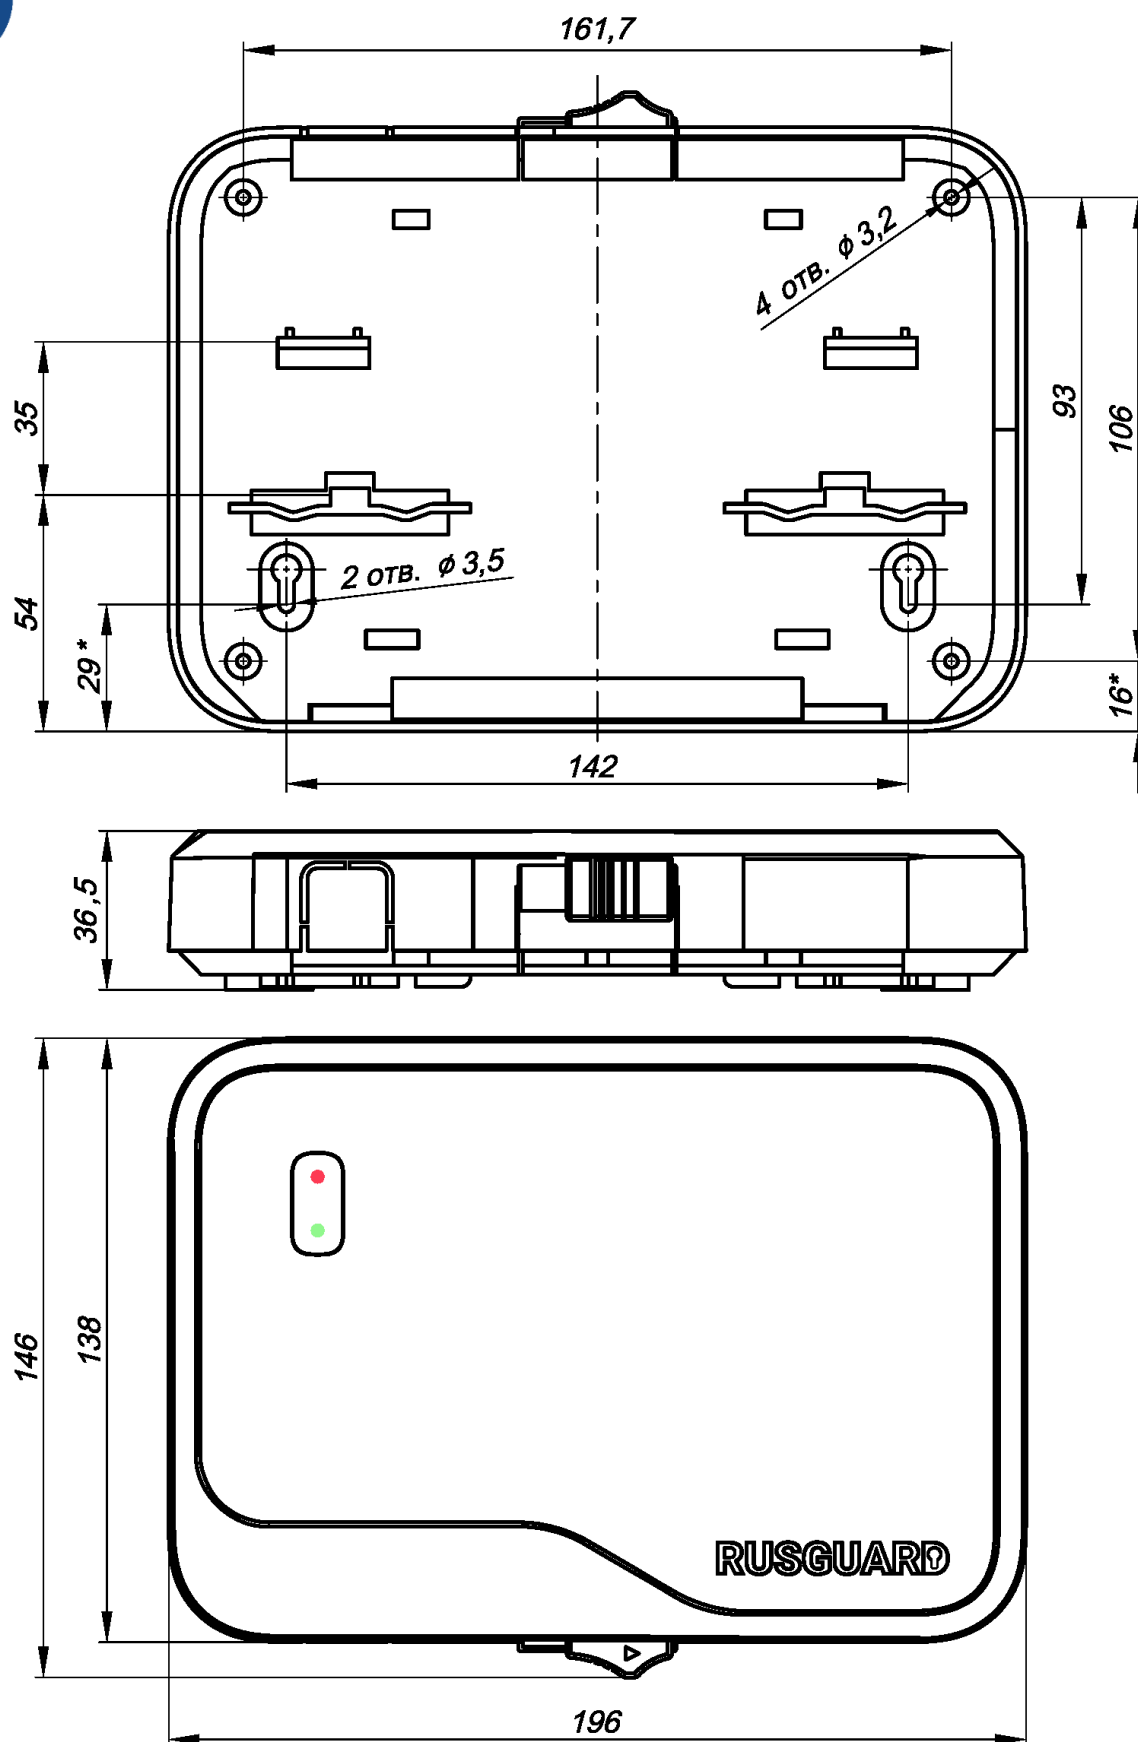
Габаритные размеры и крепёж контроллера в корпусе исполнения -S
